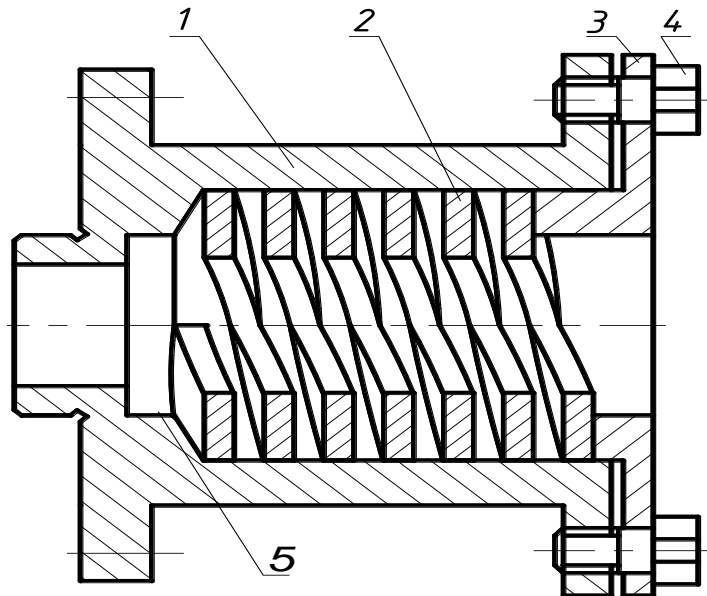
Конструкція пристрою для розточування нежорстких гвинтових деталей
